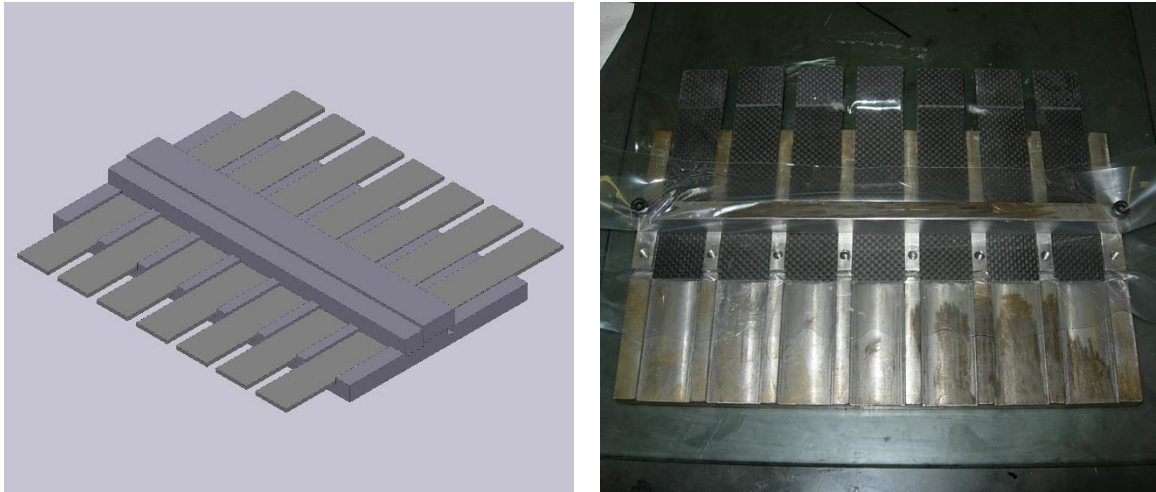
Dispositivo em aço para fabricação de juntas sobrepostas simples
